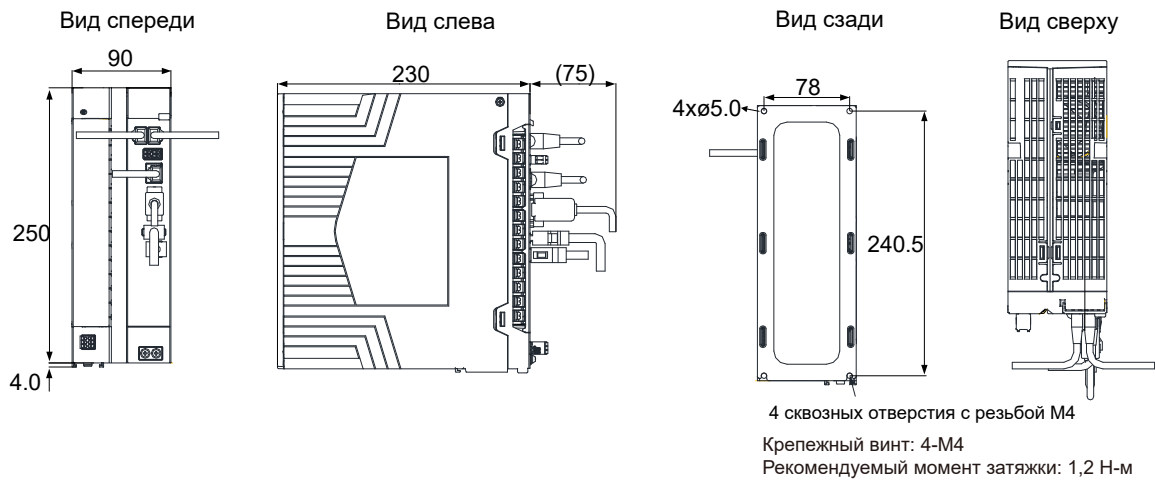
Габаритные размеры для типоразмера E (ед. изм: мм)
